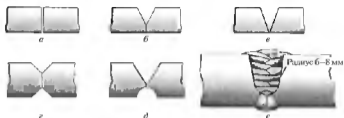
Соединения сварные стыковые: *a* — без разделки кромок, *b* — с V-образным скосом и притуплением кромок, *c* — с V-образным скосом кромок; *z* — с двусторонним V-образным скосом кромок и притуплением, *d* — с V-образным скосом и притуплением кромок; *e* — с односторонним V-образным скосом кромок.
